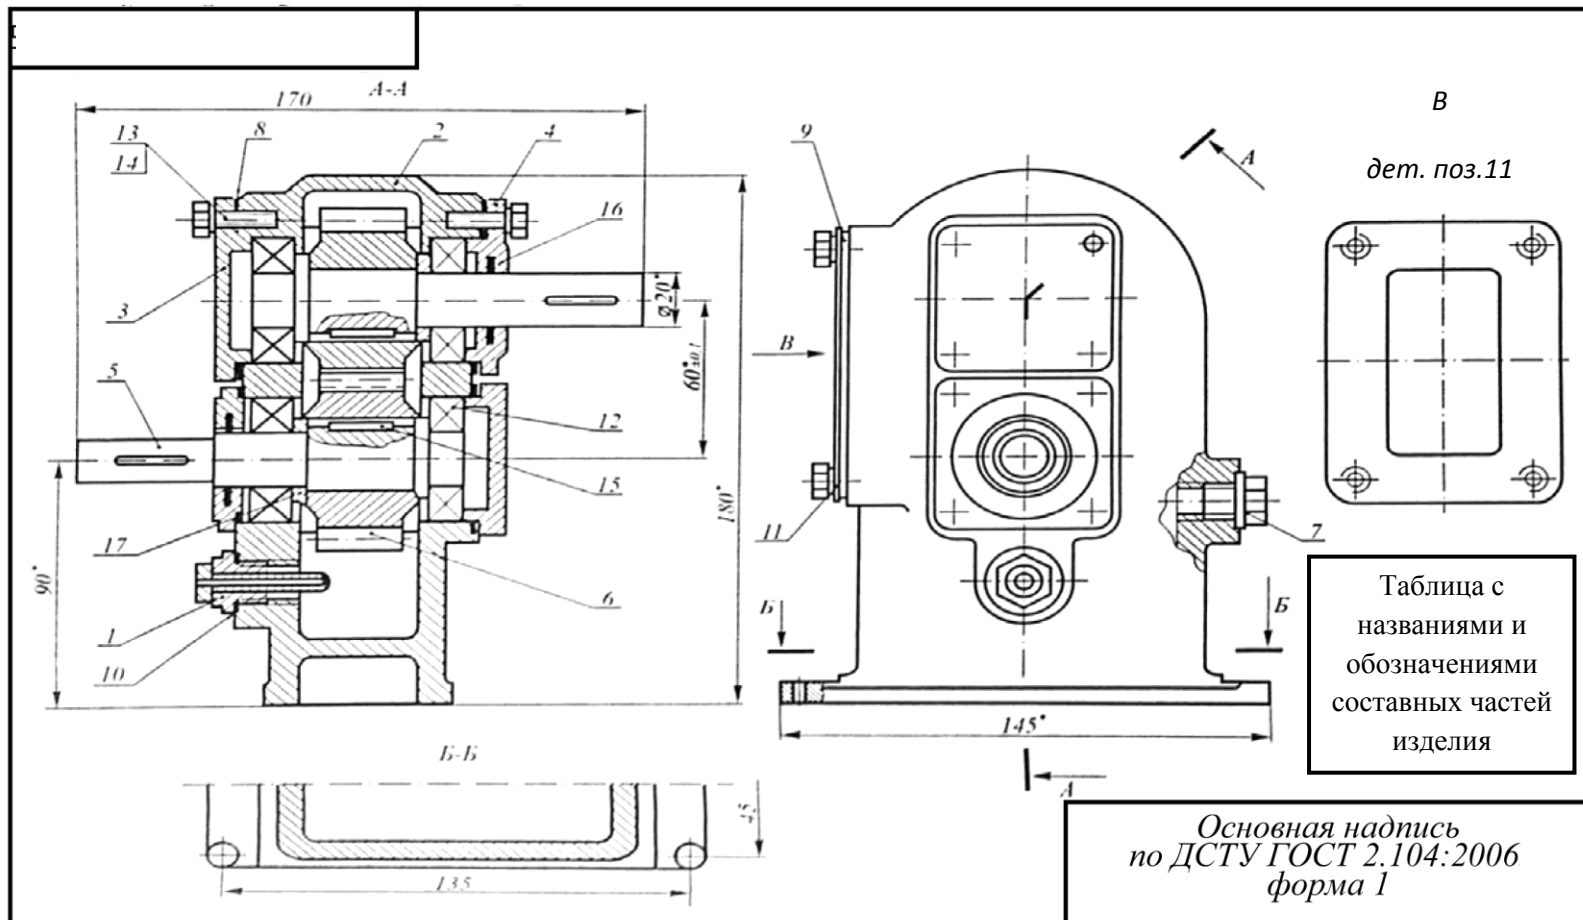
Пример оформления чертежа на общий вид редуктора
